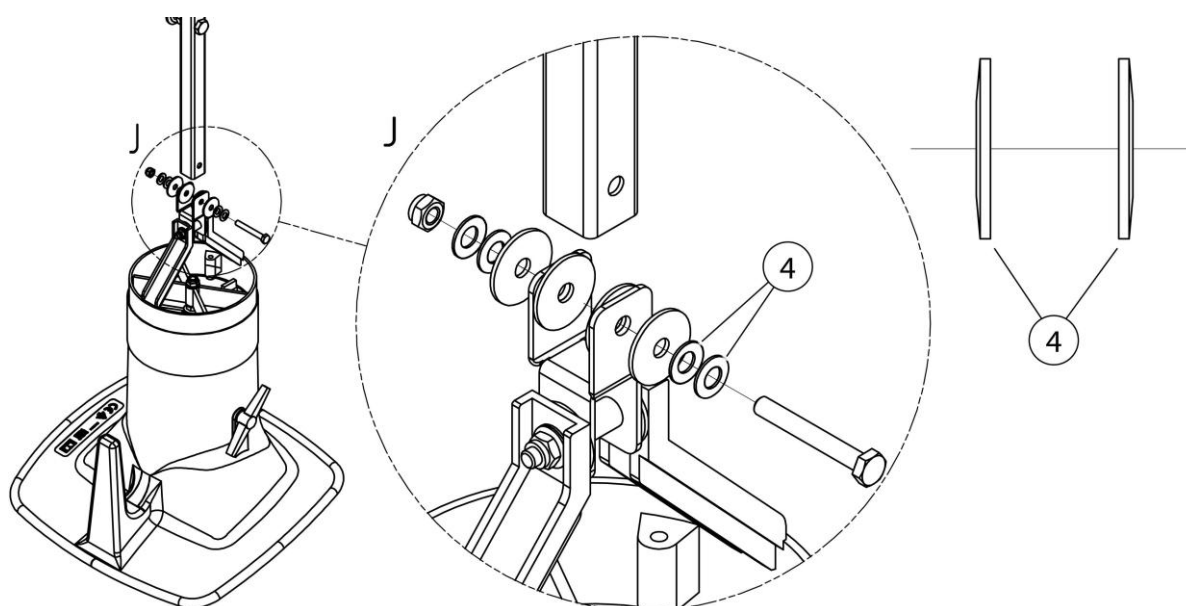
Montaje – Montar el producto con bastidor de soporte
